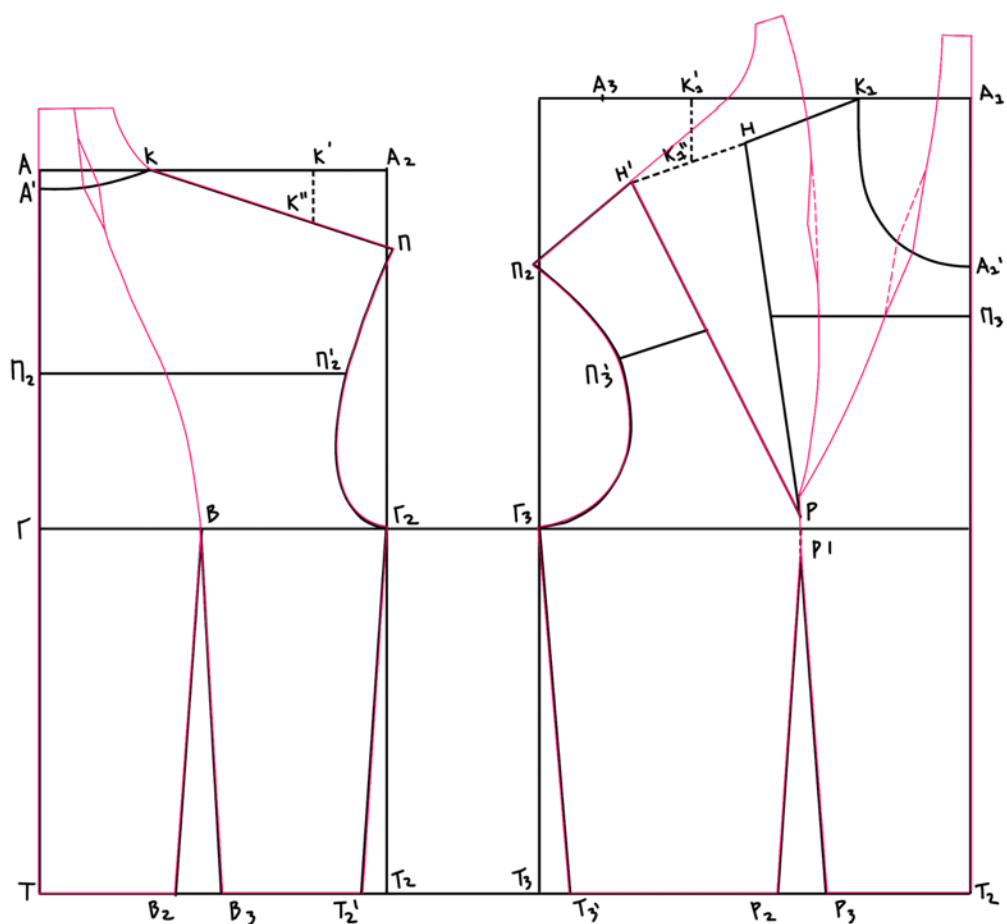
Схема побудови базового лекала та базової моделі переду і спинки блузи жіночої з вшивними рукавами 176-80-88
